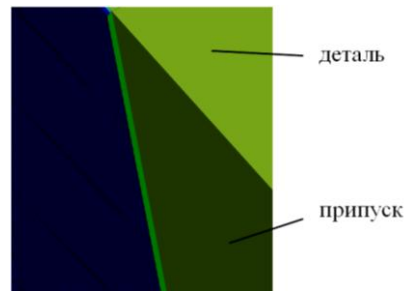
Аналіз припуску після напівчистового фрезерування призматичного заглиблення
